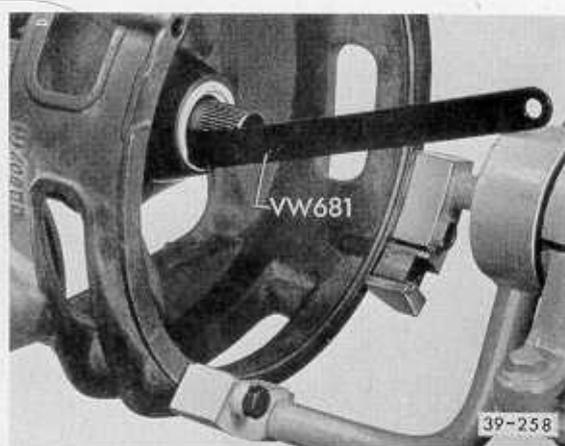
Dichtring für Drehmomentwandler heraushebeln.
